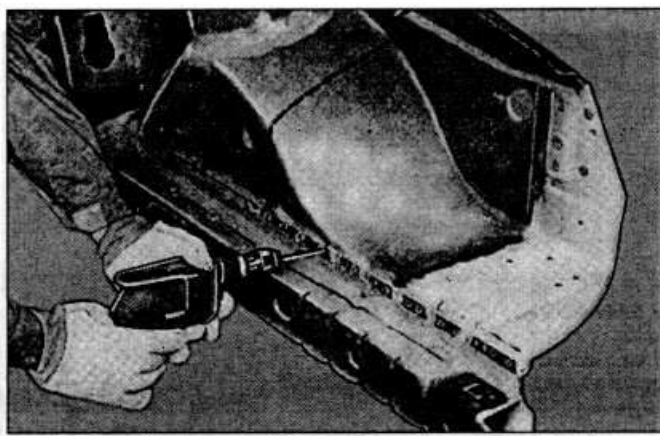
Высверливание точек контактной сварки надколесного кожуха
